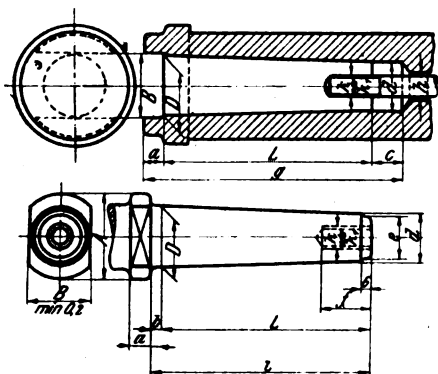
Konusbefestigung für Fräswerkzeuge.
